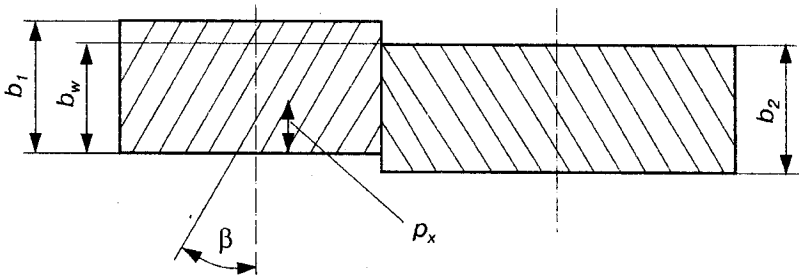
До визначення робочої ширини зубчастого вінця
